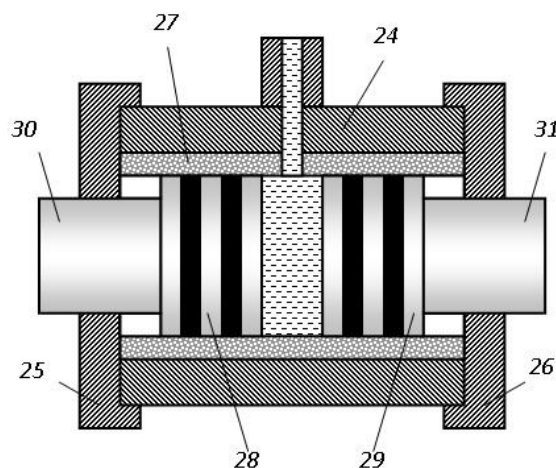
Схема тормозного механизма стенда для проведения имитационных испытаний гидроцилиндров:
